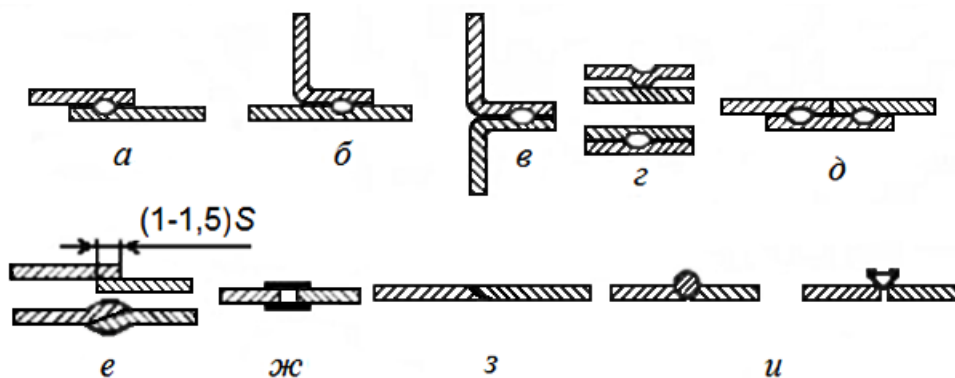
Варианты конструкции соединений шовной сварки
